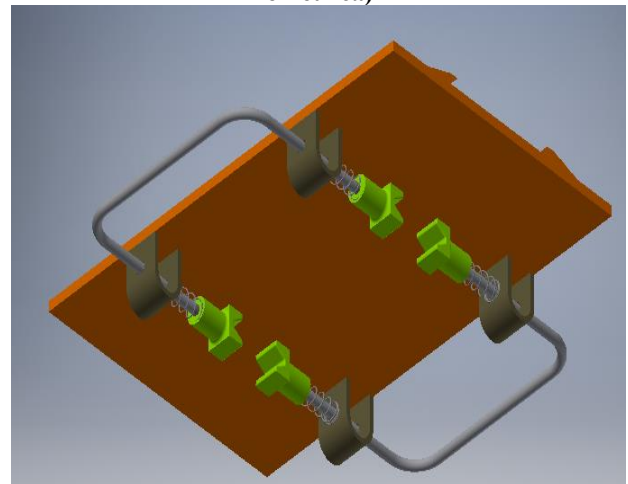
Sistem de prindere cu prisme mobile (vedere izometrică)
